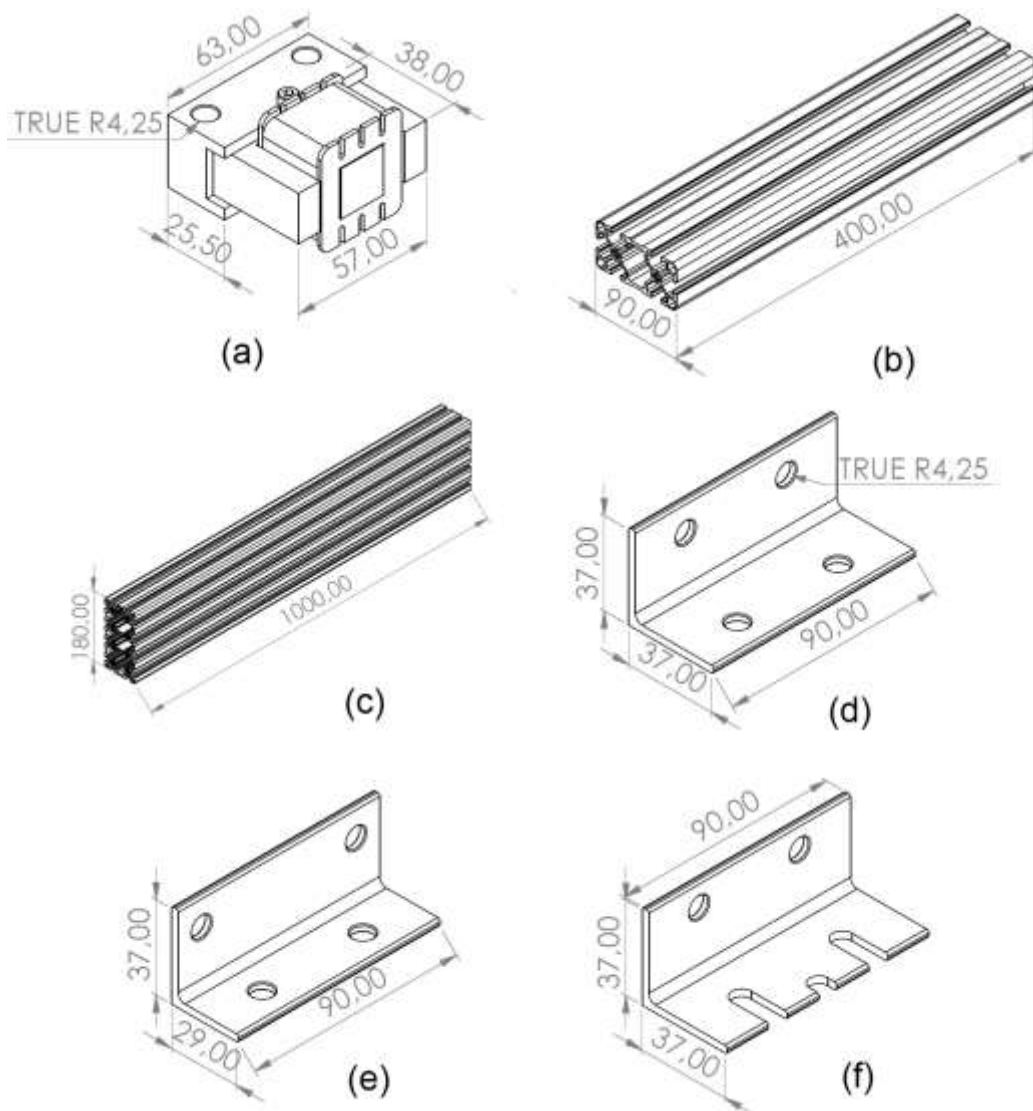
(a) Desenho atuador (b) Desenho perfil coluna (c) Desenho perfil base (d) Cantoneira (e) Cantoneira para engaste da viga (f) cantoneira com rasgo
